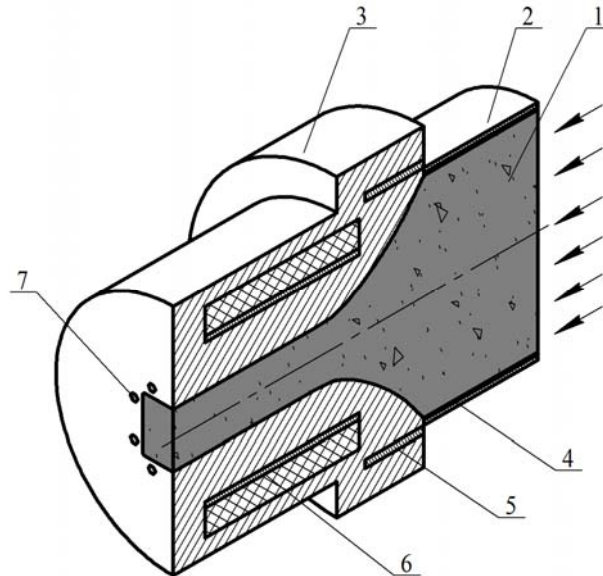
Схема прессового инструмента для формования углеродной массы методом экструзии: 1 – углеродная масса; 2 – массовой цилиндр; 3 – мундштук; 4 – нагреватель массового цилиндра, 5 – нагреватель задней части мундштука; 6 – нагреватель калибрующей части мундштука; 7 – дополнительные нагреватели
